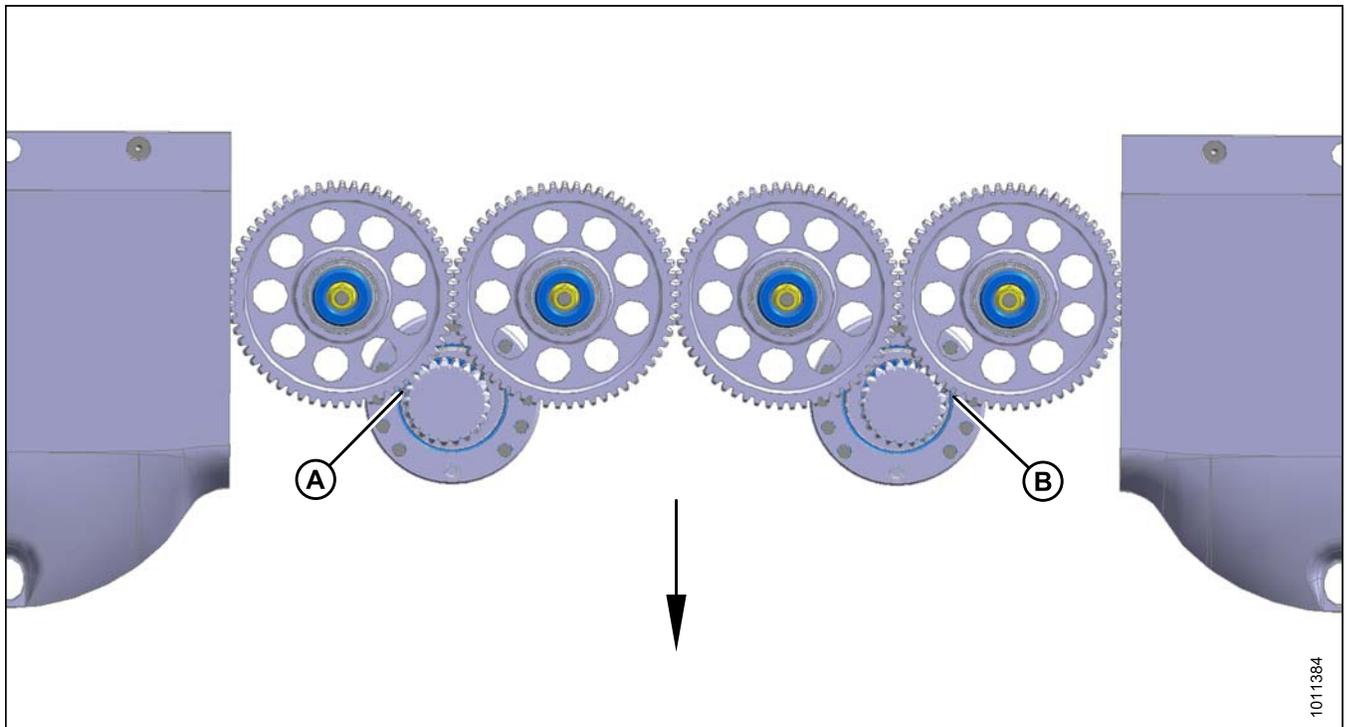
Dessous des pivots de la barre de coupe installés dans la barre de coupe
